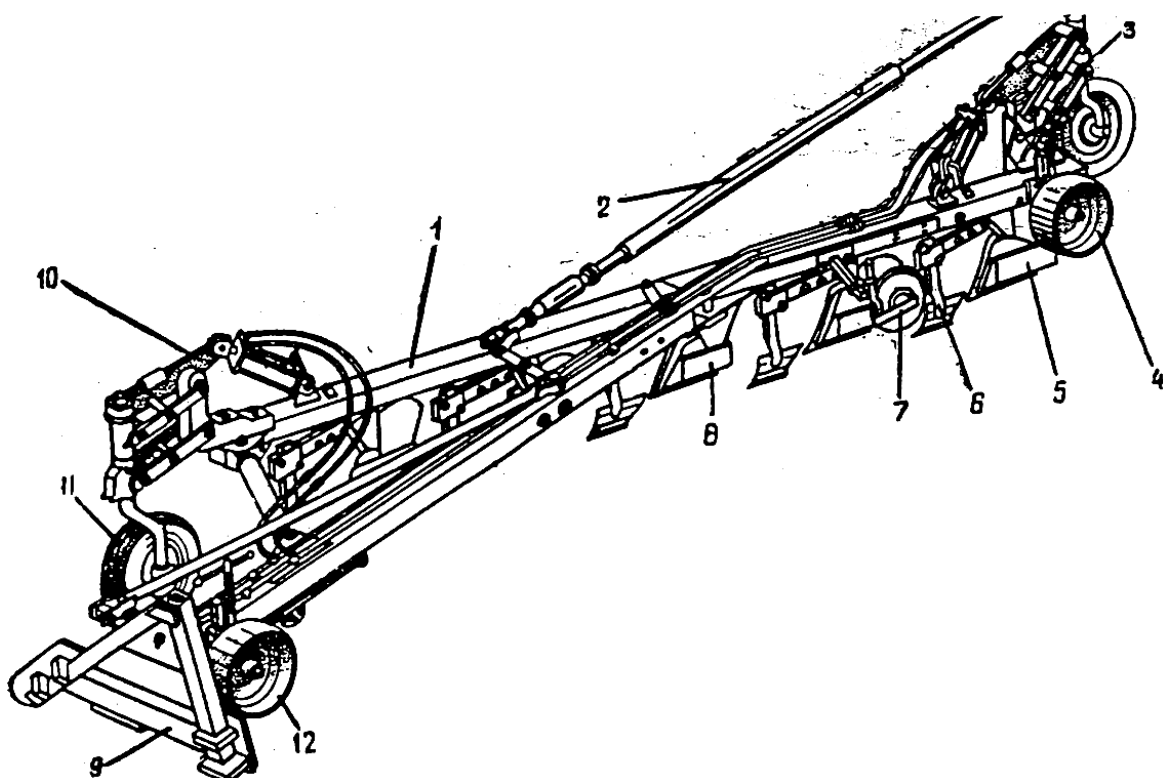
Плуг пятикорпусный полунавесной ПЛ-5-35: 1 – рама; 2 – механизм управления; 3 – механизм бороздного колеса; 4, 12 – полевой колесо; 5, 8 – корпус; 6 – предплужник; 7 – дисковый нож; 9 – подвеска; 10 – механизм переднего бороздного колеса; 11 – бороздное колесо
